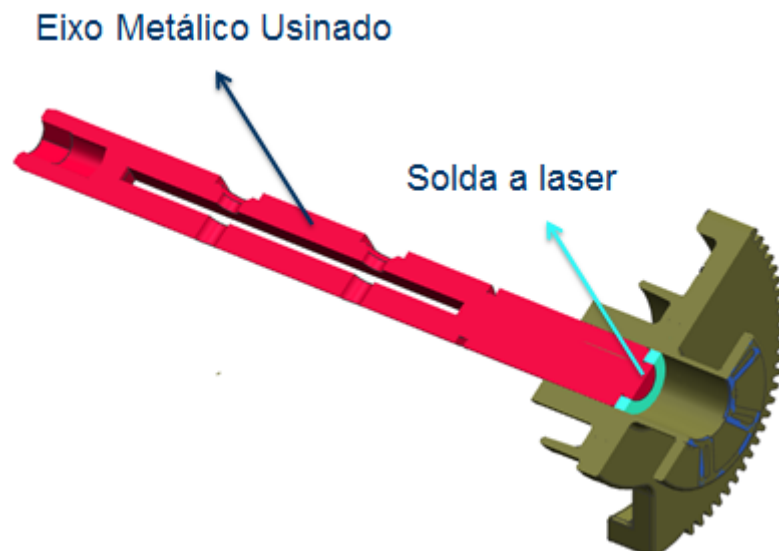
Engrenagem Plástica Parcial soldada no Eixo Metálico Usinado
